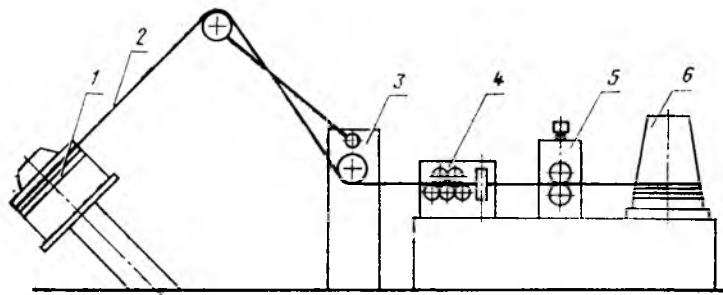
Волочильный стан для производства ромбической проволоки: 1 — фигурка; 2 — проволока; 3 — устройство для аварийной остановки стана; 4 — правильное устройство; 5 — роликовая волока; 6 — приемный барабан.
